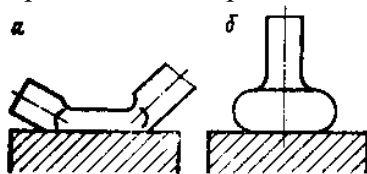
Виды термокомпрессионной сварки по способу выполнения соединения:
